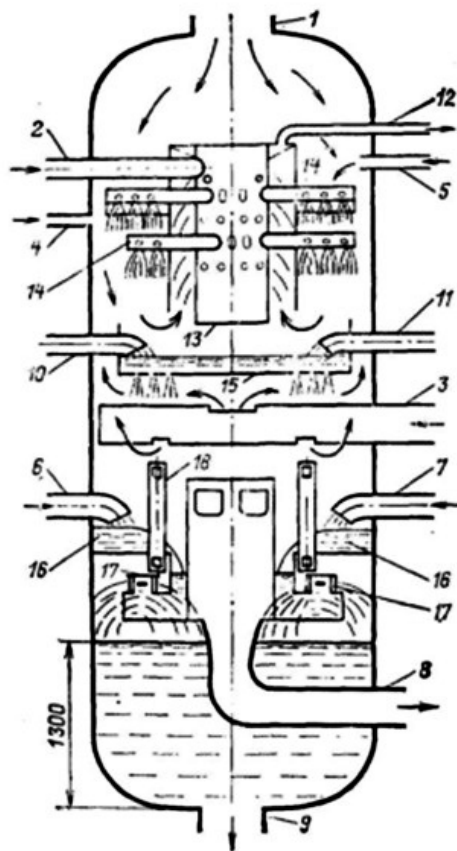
Конструкция вертикального смешивающего подогревателя:
